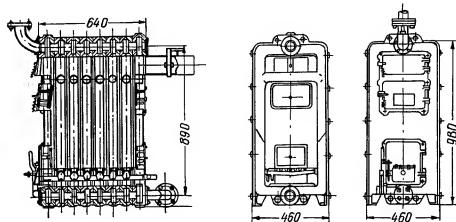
Габаритные размеры котла поверхностью нагрева $2,26\text{ м}^2$
